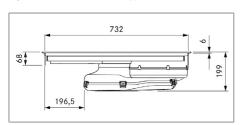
PURA dimensioni apparecchio vista frontale
